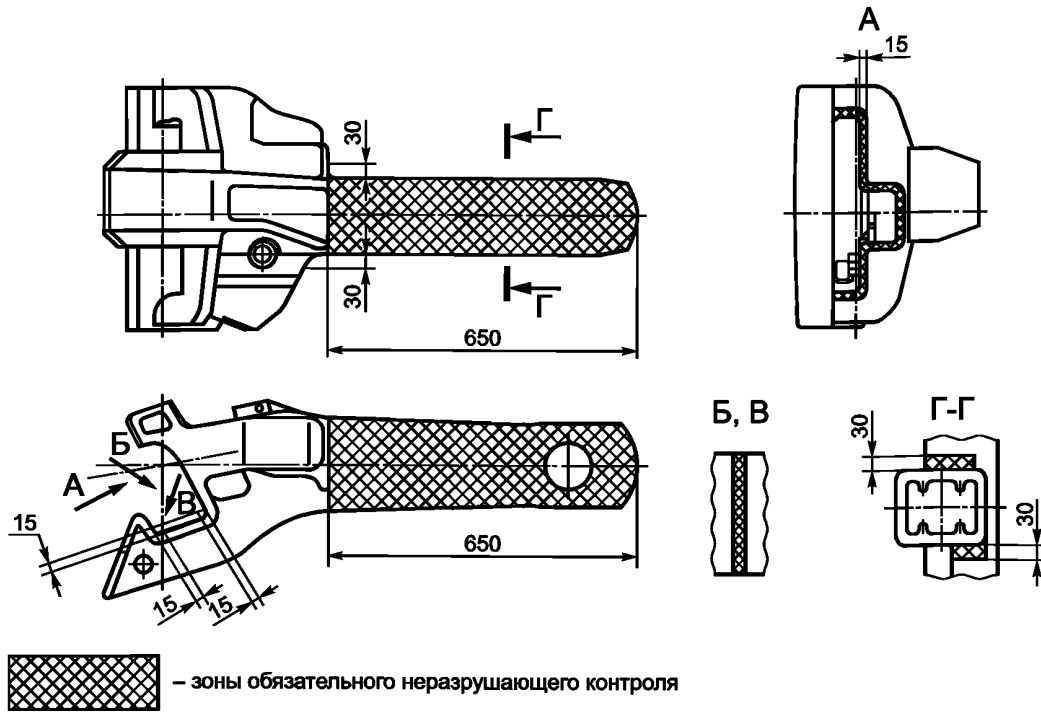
Зоны неразрушающего контроля на корпусах автосцепок СА-3Т
